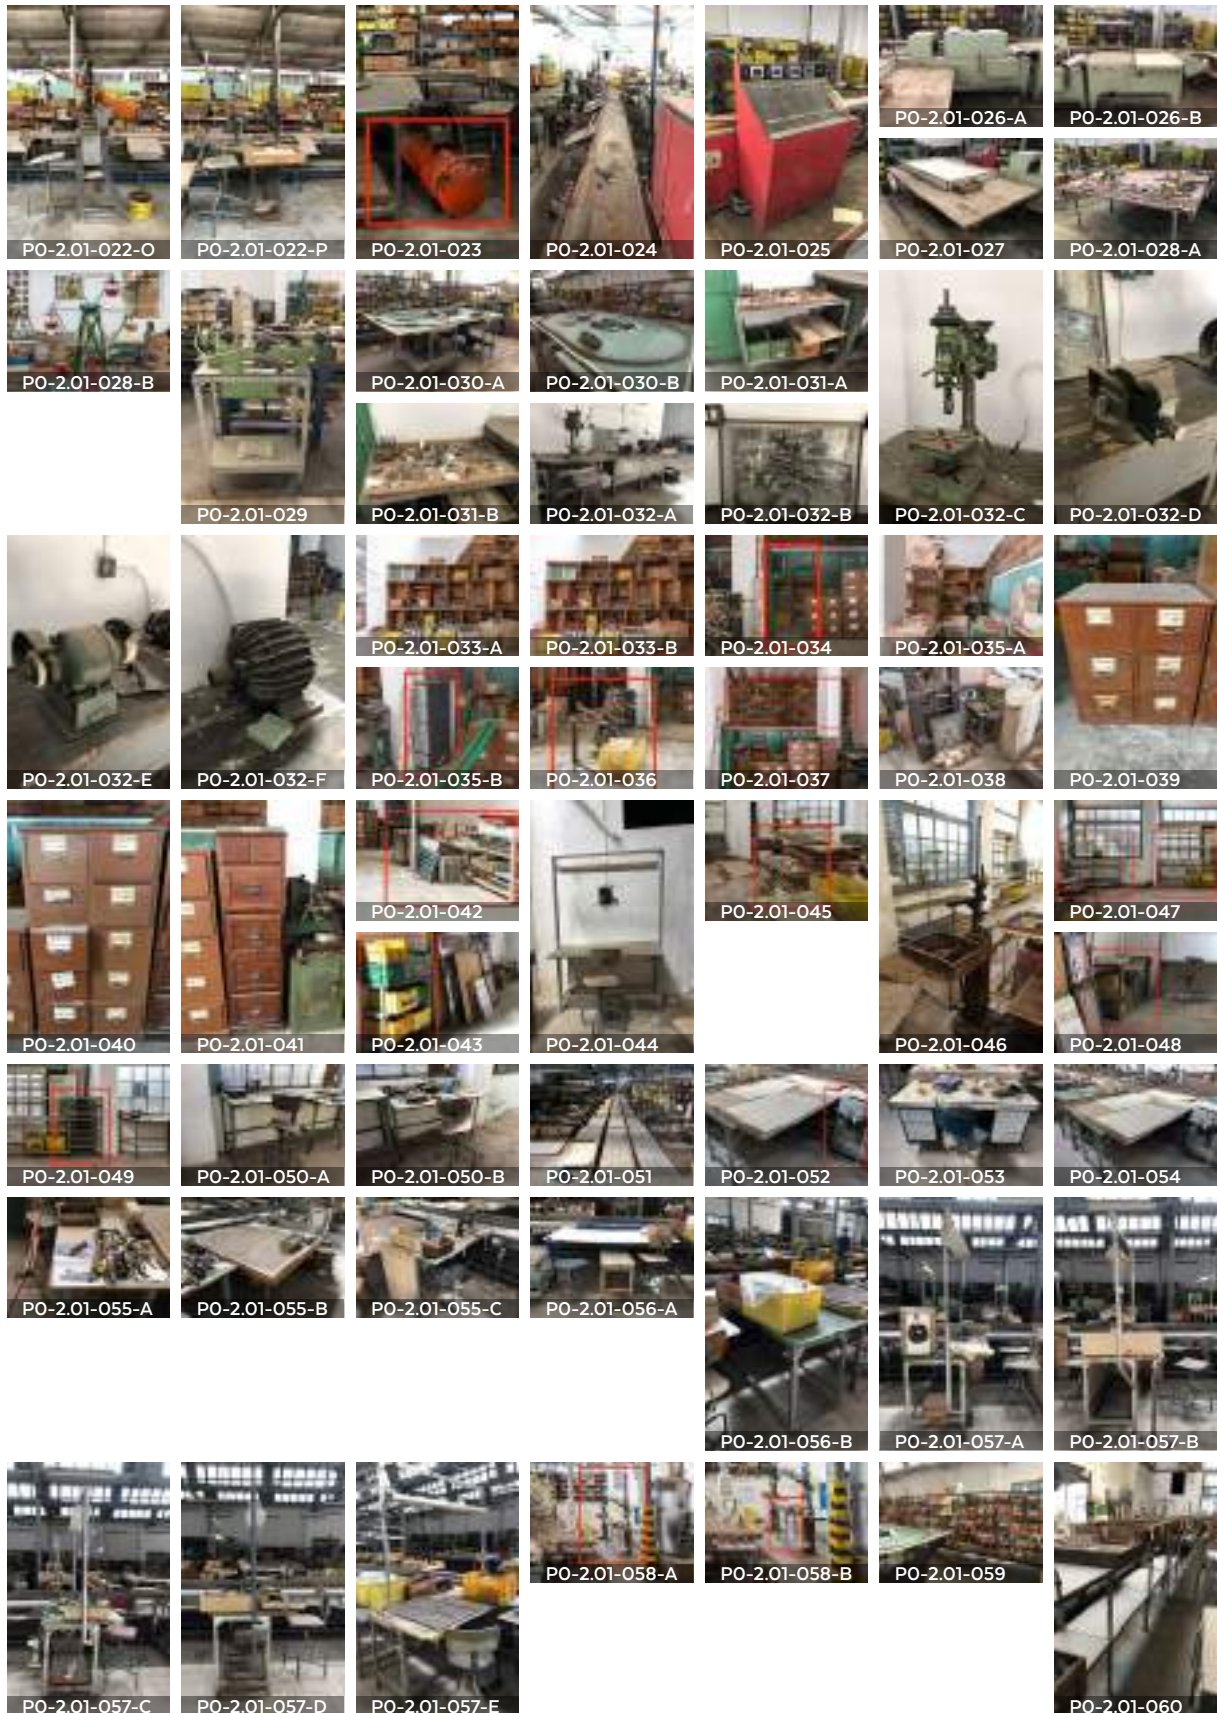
Zoom de cadena de montaje (PO-2.01)
